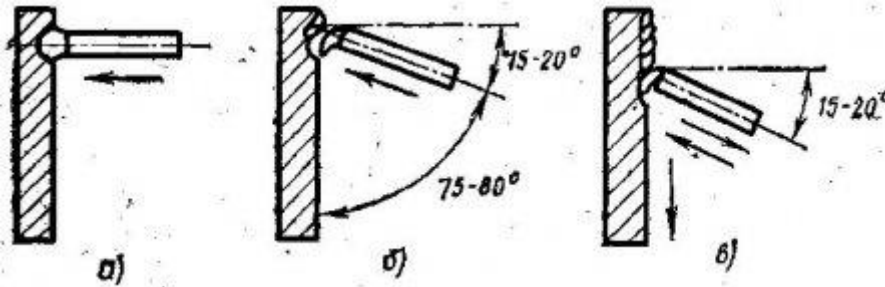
Схема техники сварки (наплавки) на спуск:
